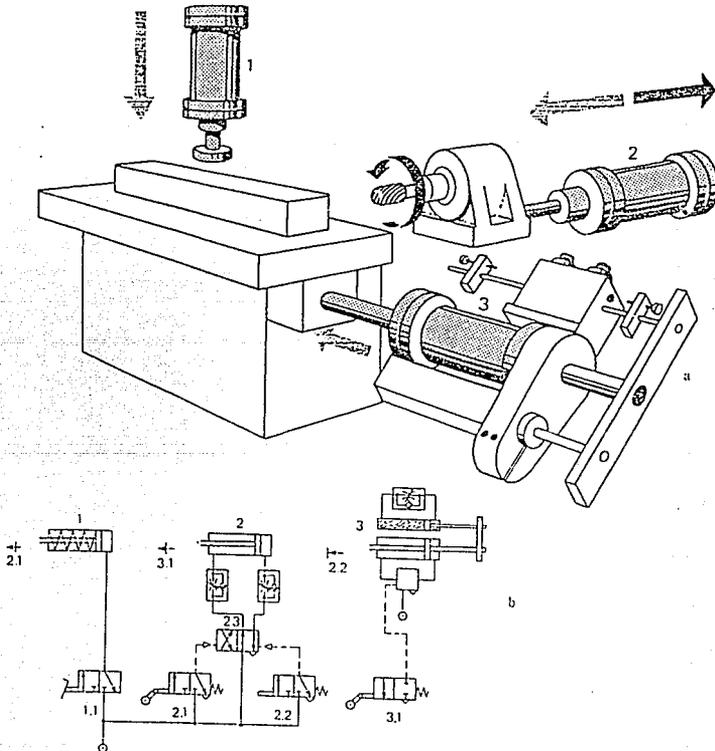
MAQUINA ESPECIAL PARA FRESAR UNA RANURA.
